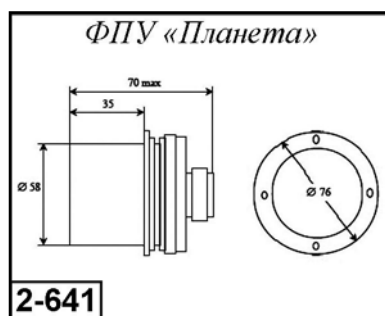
Внешний вид и габаритные размеры ФПУ «Планета»
